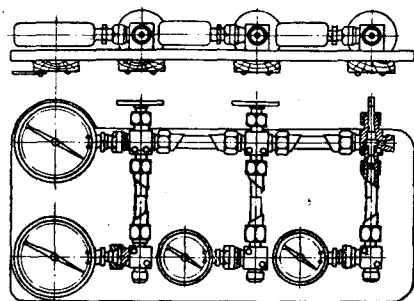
Компрессор среднего давления: 1 — компрессор; 2 — двигатель; 3 — редуктор; 4 — рама; б) — трехрожковый воздухораспределительный щит
